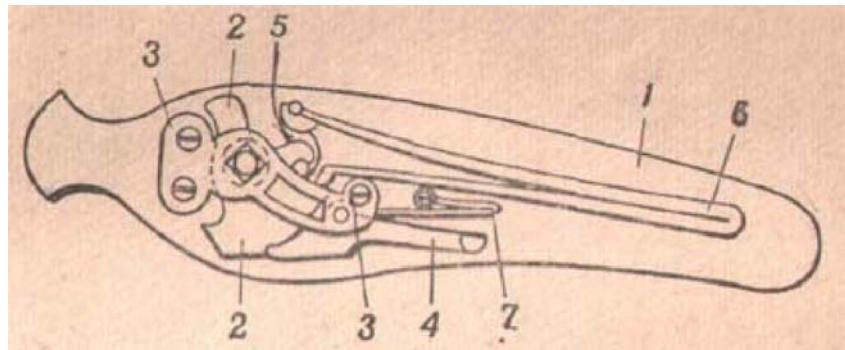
Обратный, или так называемый замок "в шейку", с наружным курком: 1 - замочная доска; 2 - лодыжка; 3 - боевая личинка (стойка); 4 - шептало; 5 - цепочка; 6 - боевая пружина; 7 - пружина шептала
